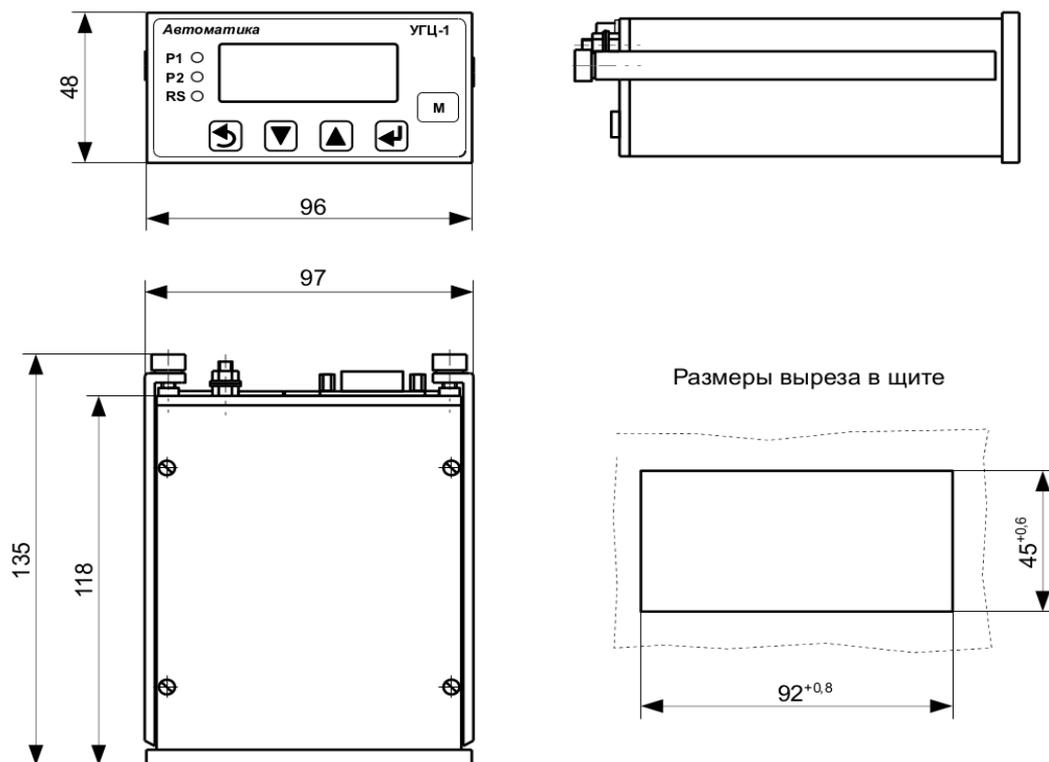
Габаритные размеры измерительного прибора щитового исполнения
